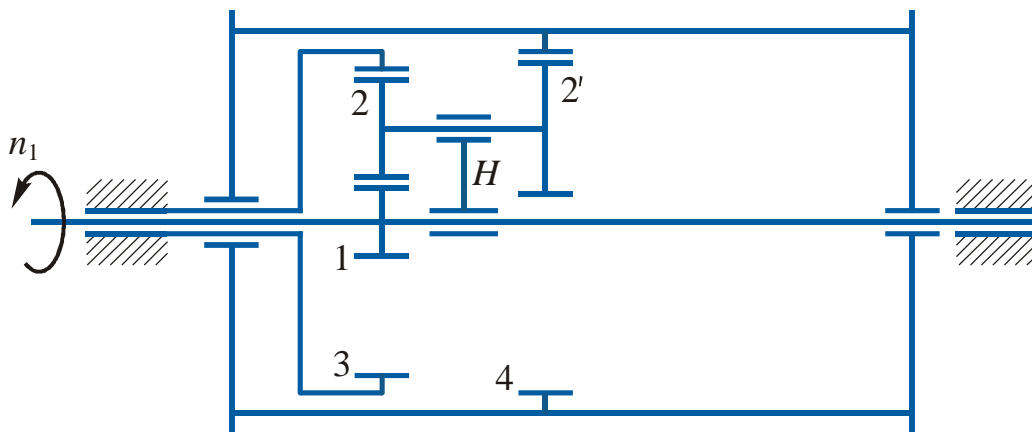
Кинематическая схема планетарного редуктора: 1 — центральная шестерня; 2 и 2' — шестерни спаренного сателлита (показан один сателлит из трех); 3 — неподвижное корончатое колесо; 4 — корончатое колесо, связанное с барабаном;  $H$  — водило
